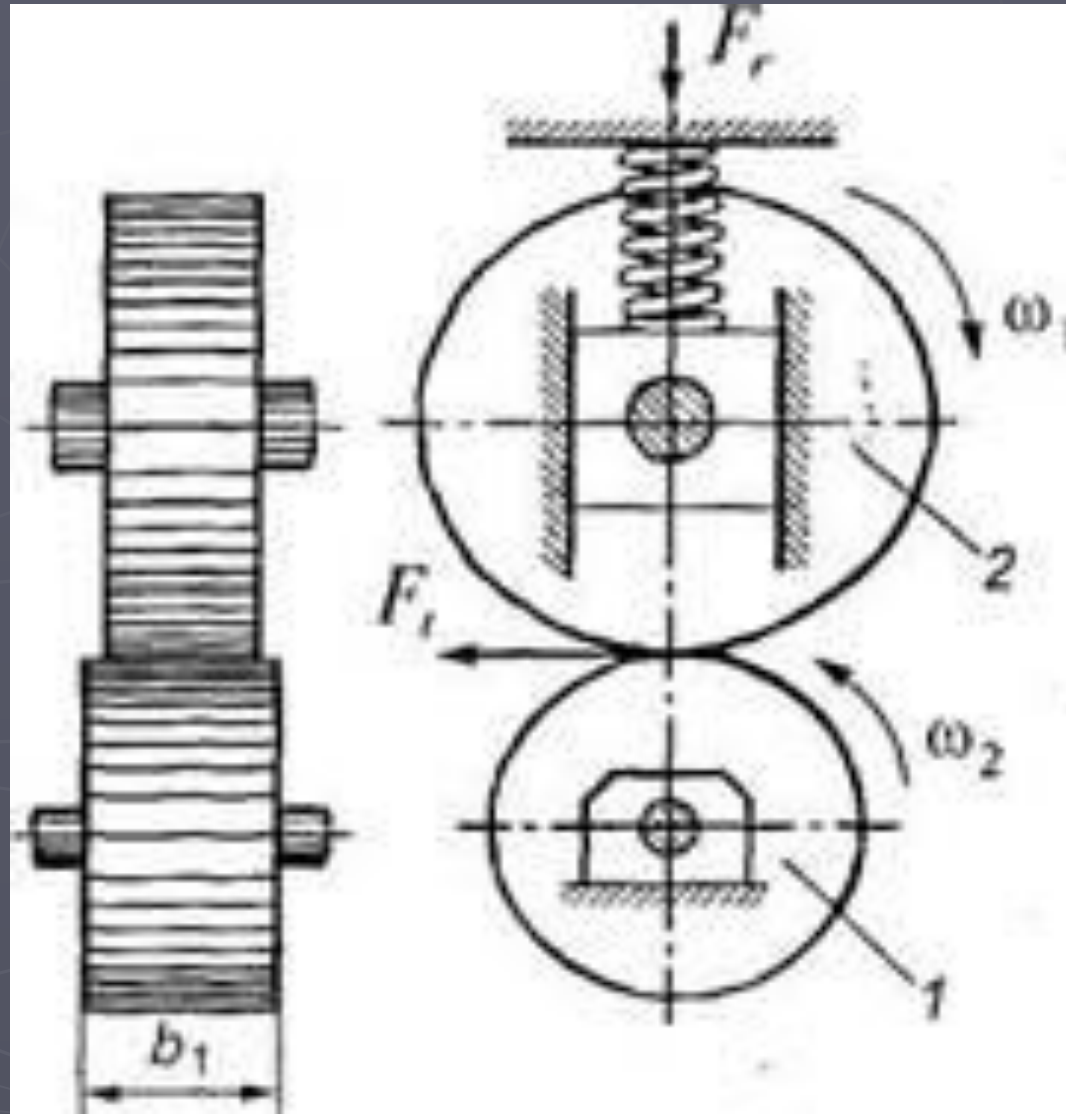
Цилиндрическая фрикционная передача с катками клинчатой формы
